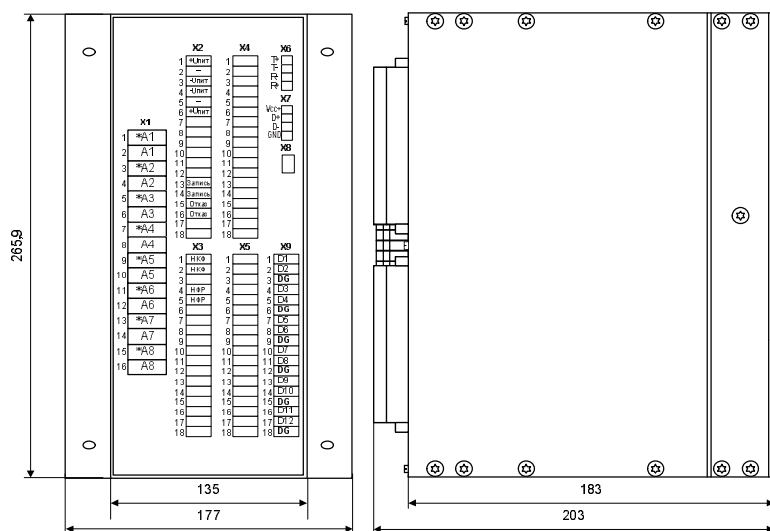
Габаритные и установочные размеры терминала автоматики ДГР «Бреслер 0107.060».
